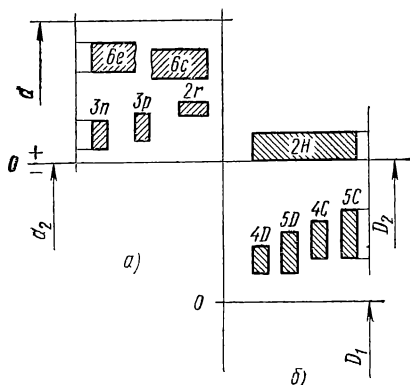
Схема расположения полей допусков для посадок резьб с натягами:
